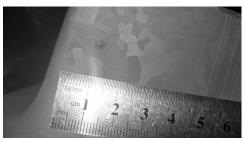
Зоны отливки рабочей лопатки 4-й ступени
